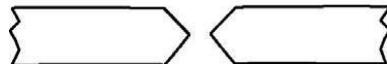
Подготовка краев заготовок при сварке встык
